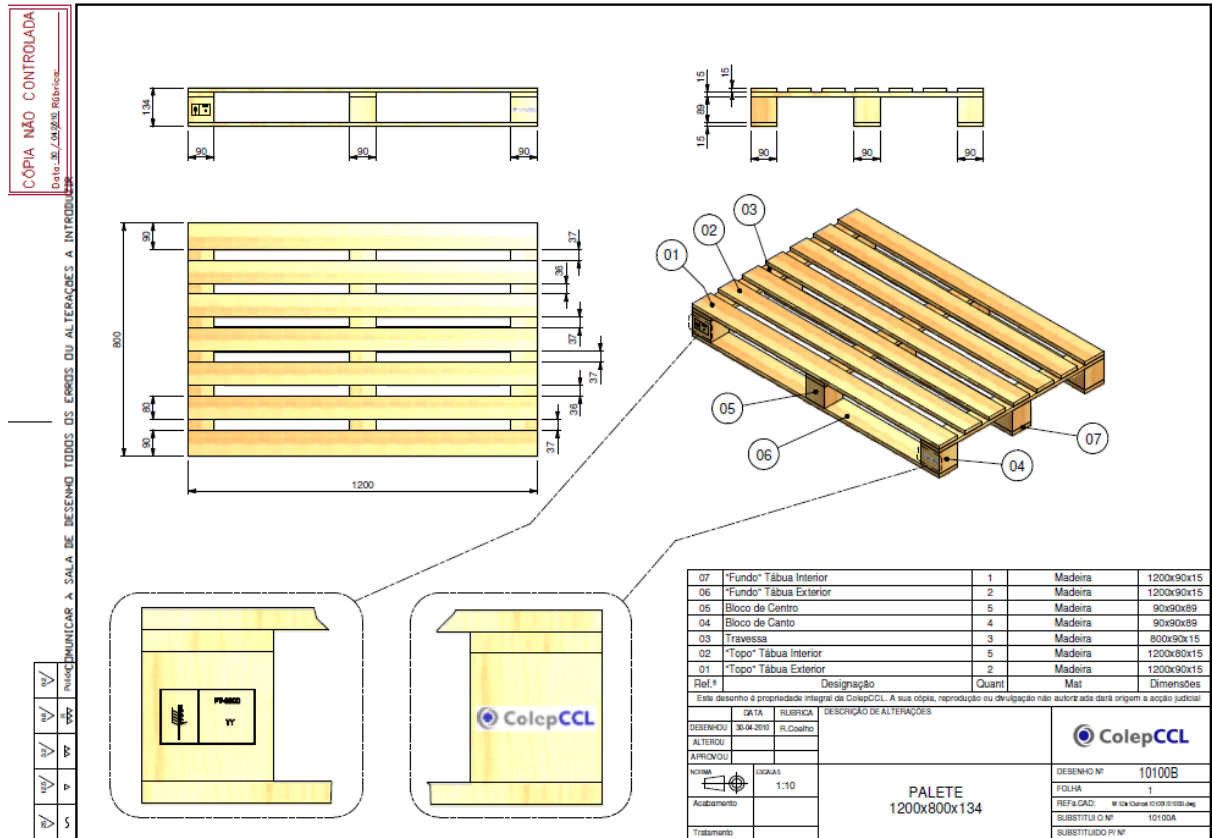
Exemplo de Desenho Técnico de uma paleta.
